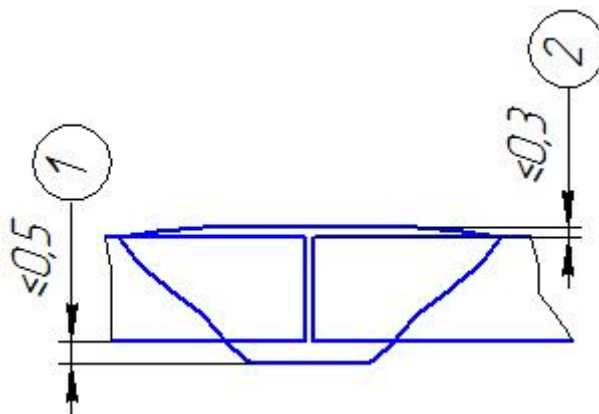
Механическая обработка сварного шва после сварки
